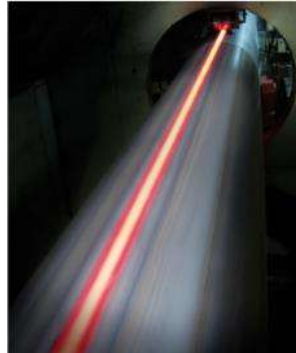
Tubo soldado longitudinalmente [27].
